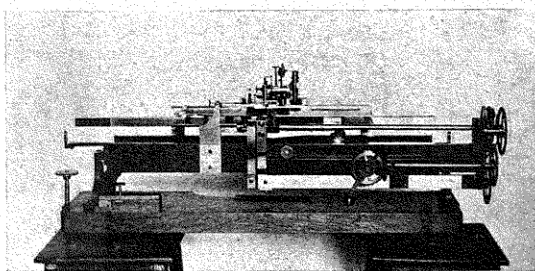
Machine à diviser la ligne droite, de *Gambey*.
